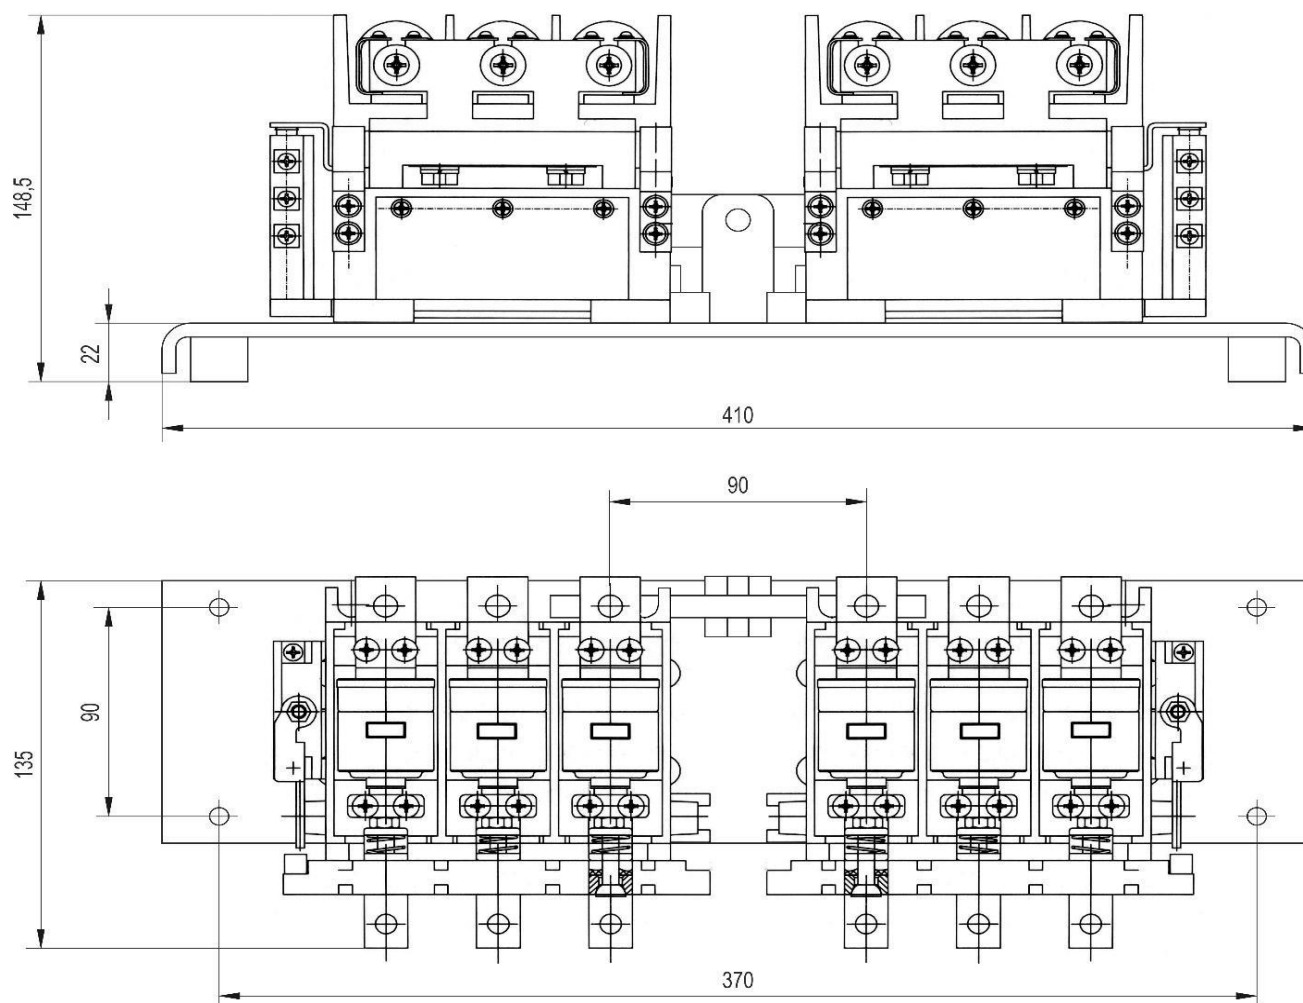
Габаритные размеры КВТ(Р)-1,14-80/125/160.
